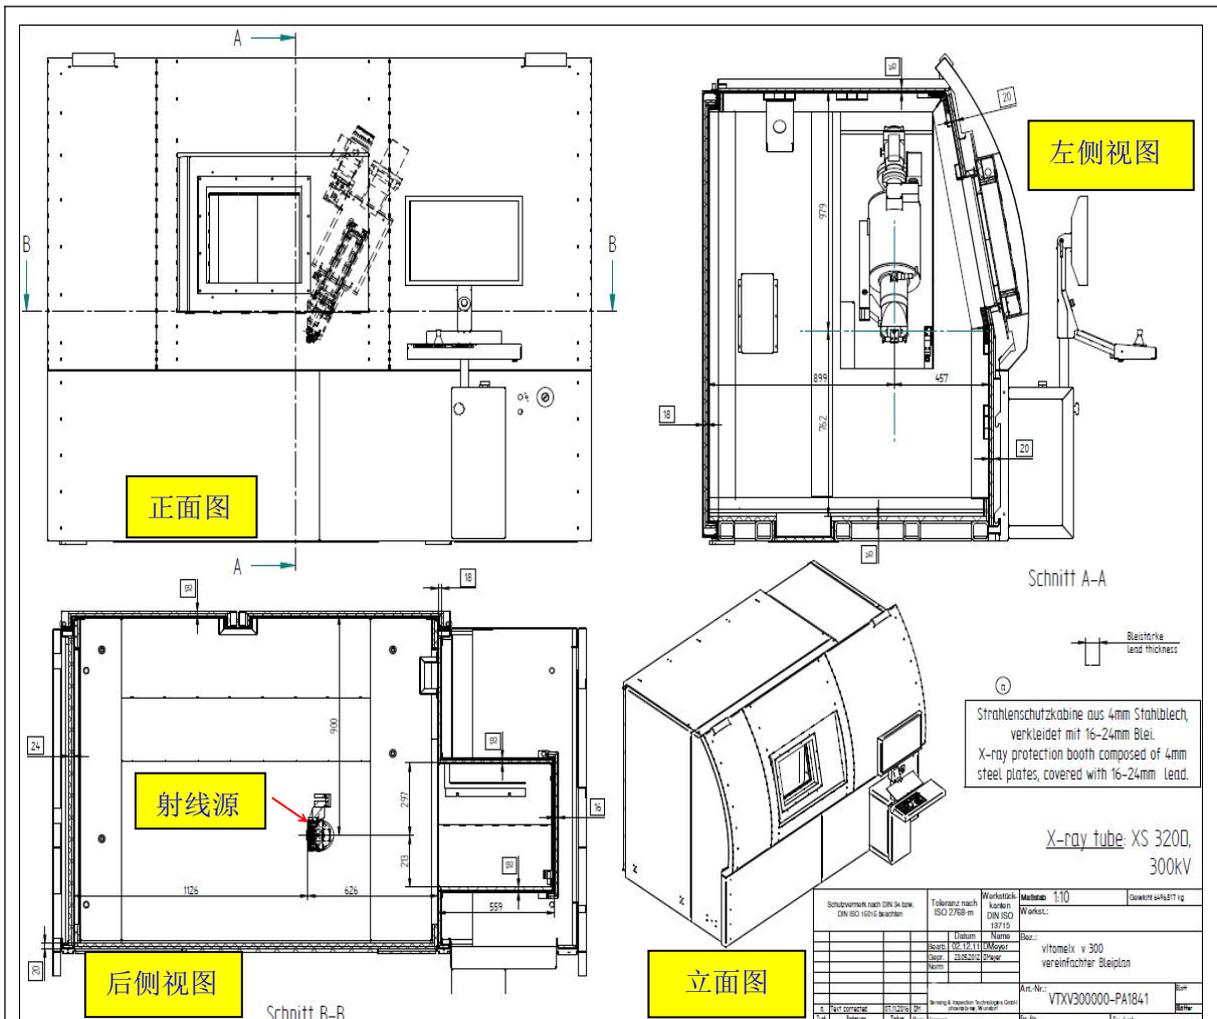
屏蔽铅房平面及剖面示意图（单位：mm）
